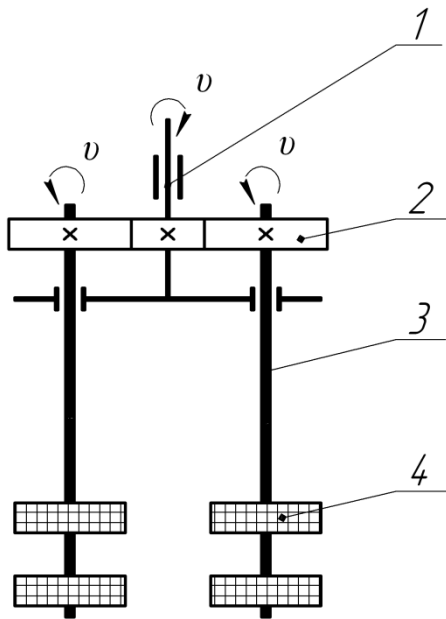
Исполнительный механизм «резервуар» в технологической системе «резервуар с абразивной средой – приспособление с обрабатываемыми деталями»
